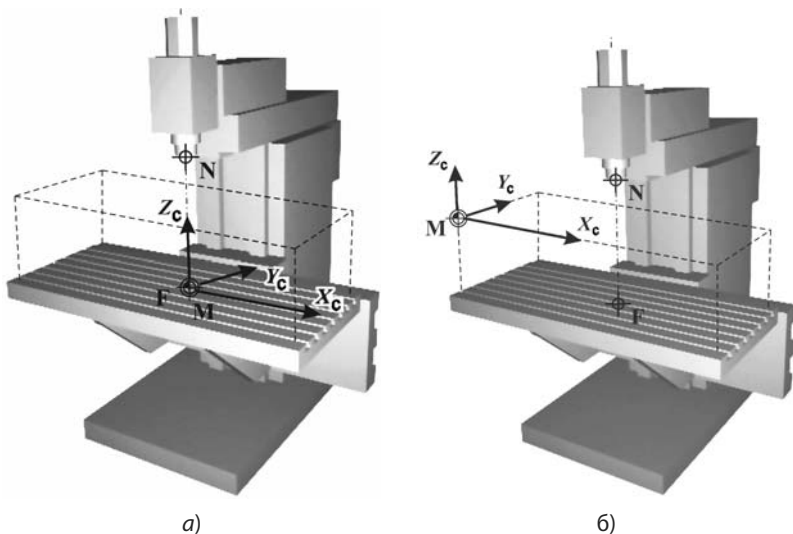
Позиция нулевой точки M на фрезерном станке:
